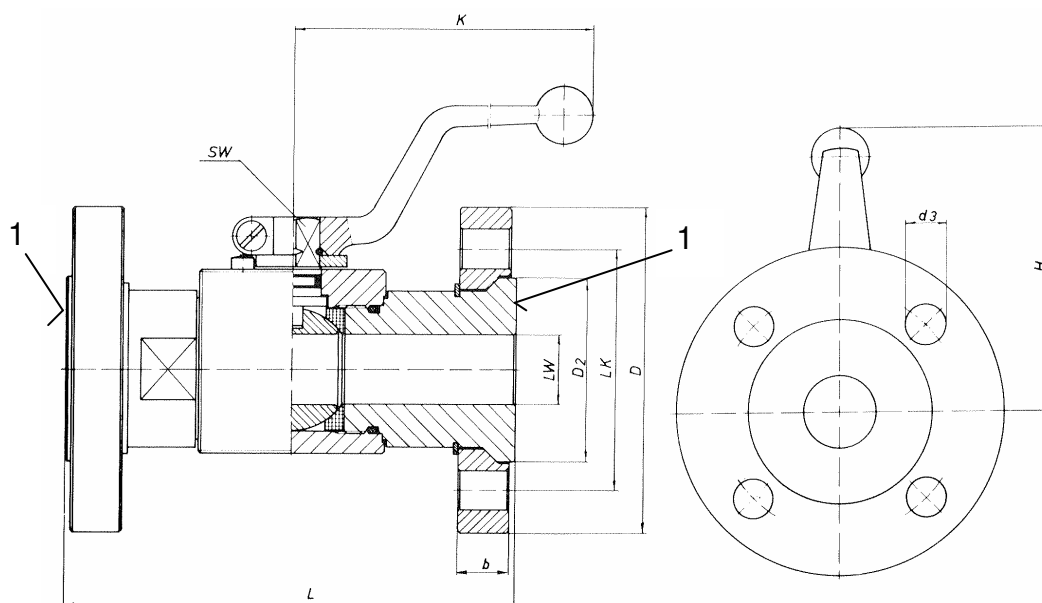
Jiná konstrukce podobného ventilu pro montáž do potrubí (Parker)
